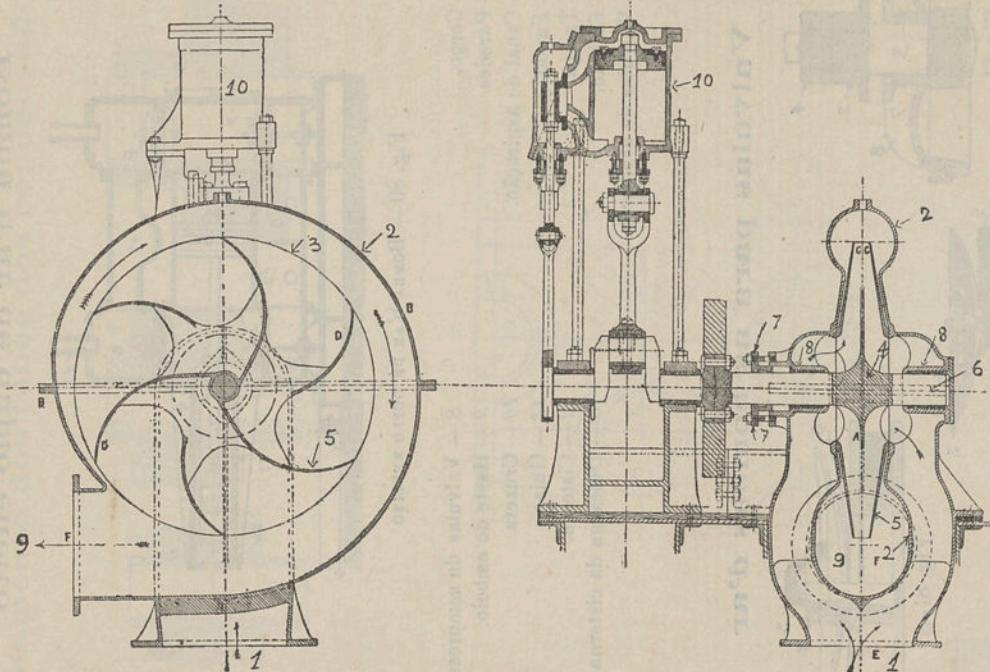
BOMBA DE CIRCULAÇÃO CENTRÍFUGA, COM MOTOR PRÓPRIO
